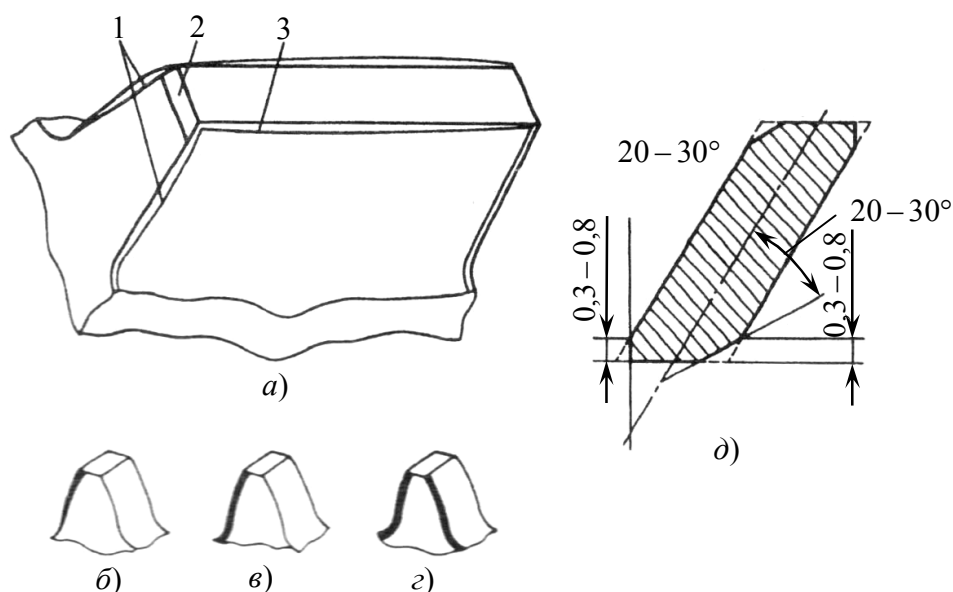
Формы фасок на зубьях цилиндрических зубчатых колес:
